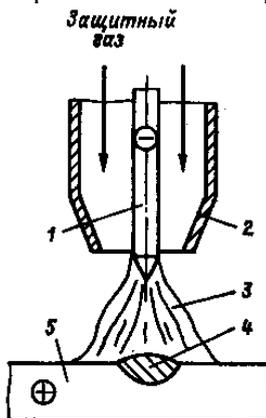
Схема процесса сварки в среде защитных газов неплавящимся электродом:
